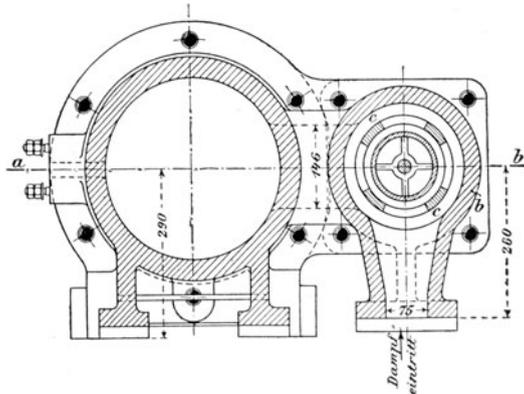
Dampfhammer mit Brinkmann-Steuerung.
